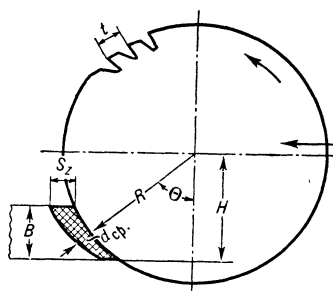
Схема процесса фрезерования: B — толщина материала; R — радиус окружности резания; t — шаг зубьев; θ — угол встречи; S_z — подача на 1 зуб.
